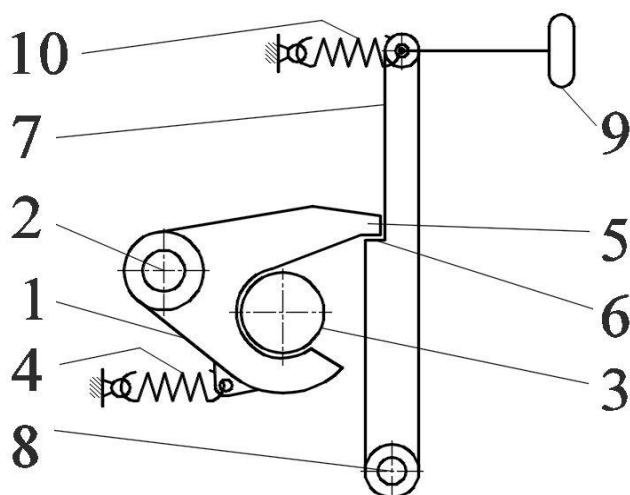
Схема запорного механізму сідельно-зчіпного пристрою.
